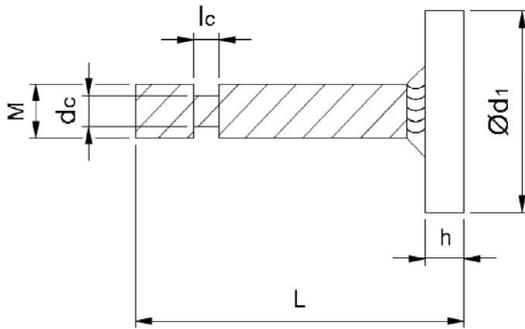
Standardausführung Drucklager aus nichtrostendem Rundstahl S690 bzw. A4-80 oder B500 NR jeweils mit Teil- oder Vollgewinde mit angeschweißter Ankerplatte S235
